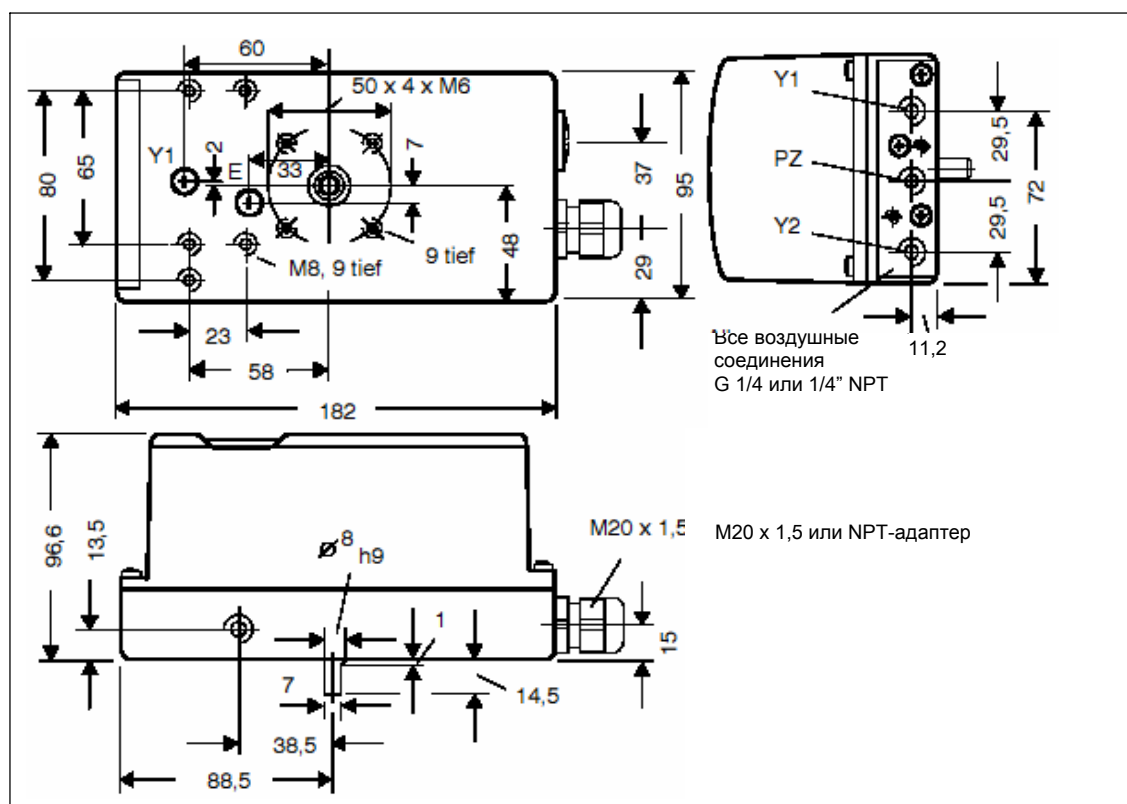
Габаритный чертеж конструкции в пластиковом корпусе 6DR5xx0
